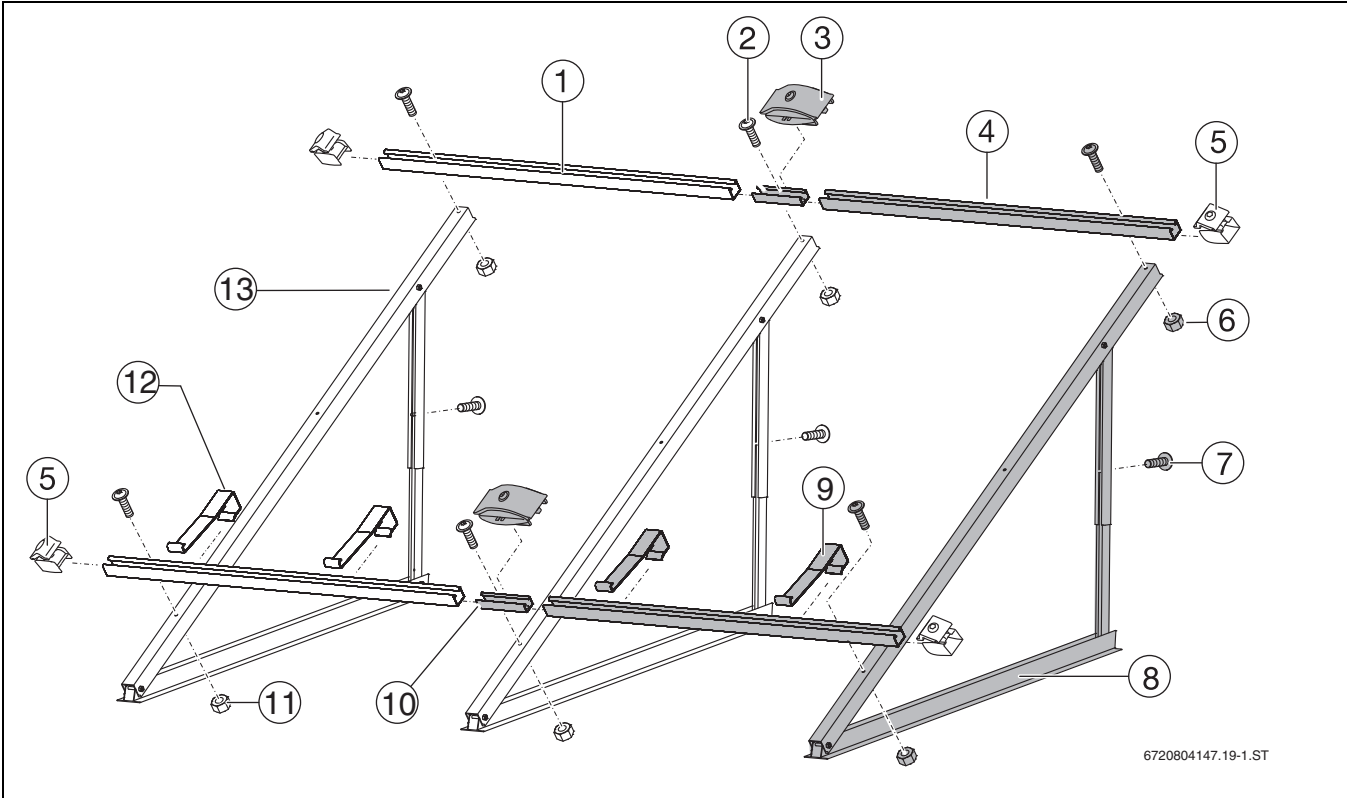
Montage-Set für 2 senkrechte Kollektoren: 1 Montage-Set Grundaufbau, 1 Montage-Set Erweiterung (grau)
